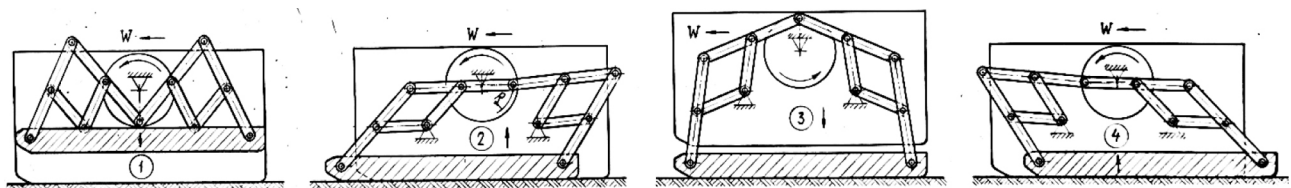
Схема процесса передвижения шагающего механизма конструкции А.М. Иванова [18]
